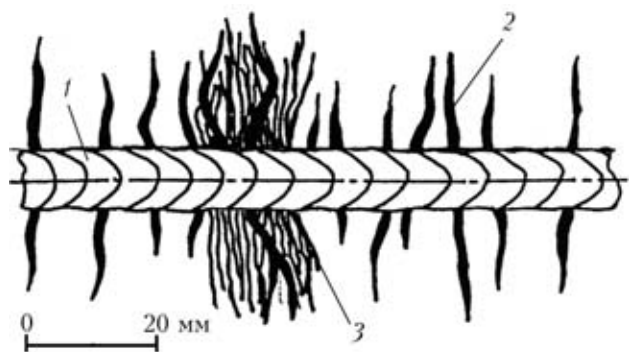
Картины ПЧЛ, полученных на образцах стыкового соединения стали Ст3: 1 — шов; 2 — прилегающая к шву зона после сварки; 3 — то же + ЭДО
